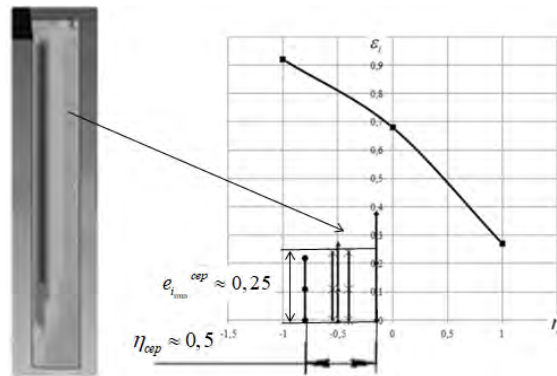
Шляхи деформування, що характерні для вісі заготовки при фіксованому натягові заготовок із сплаву W-Ni-Fe при різних значеннях кута нахилу матриці.
